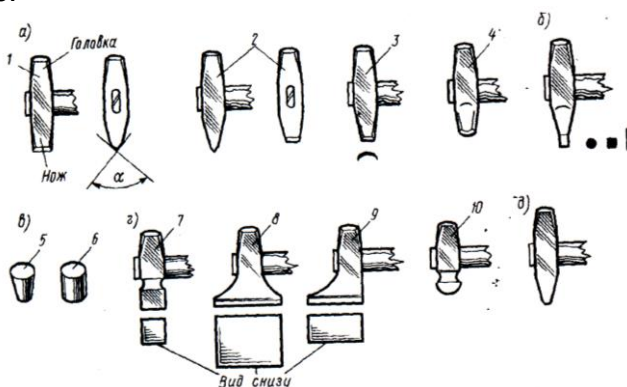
Подкладной инструмент первой группы: а – зубила (1 – для поперечной рубки; 2 – для продольной рубки; 3 – радиусные; 4 – фасонные); б – пробойник; в – прошивки (5 – конический; 6 – цилиндрический); г – гладилки (7 – с квадратной рабочей поверхностью; 8 – с увеличенной поверхностью; 9 – с одной стороной прямоугольной поверхностью; 10 – с цилиндрической поверхностью); д – раскатка
